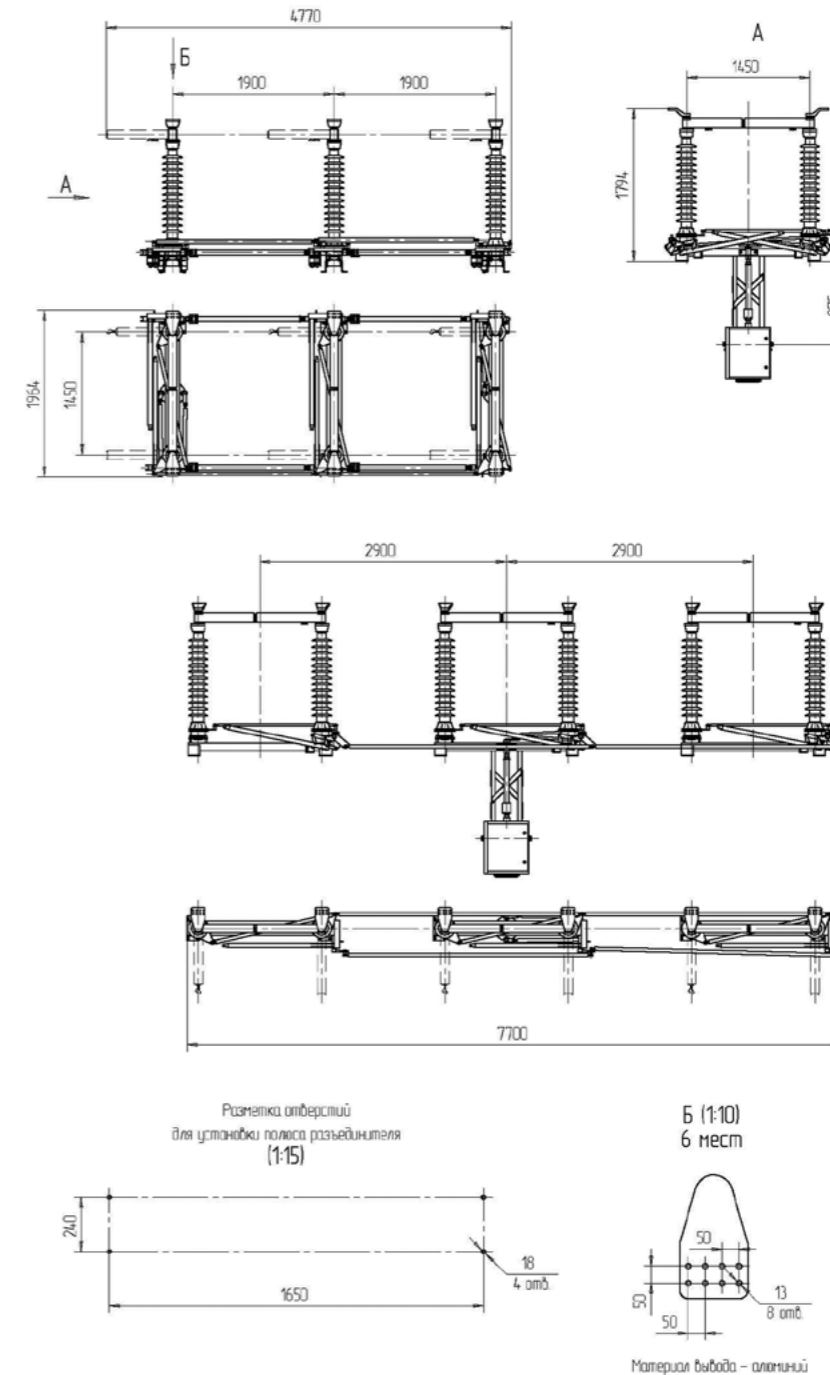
Габаритные и установочные чертежи разъединителя ONIII-123/1600/U2
